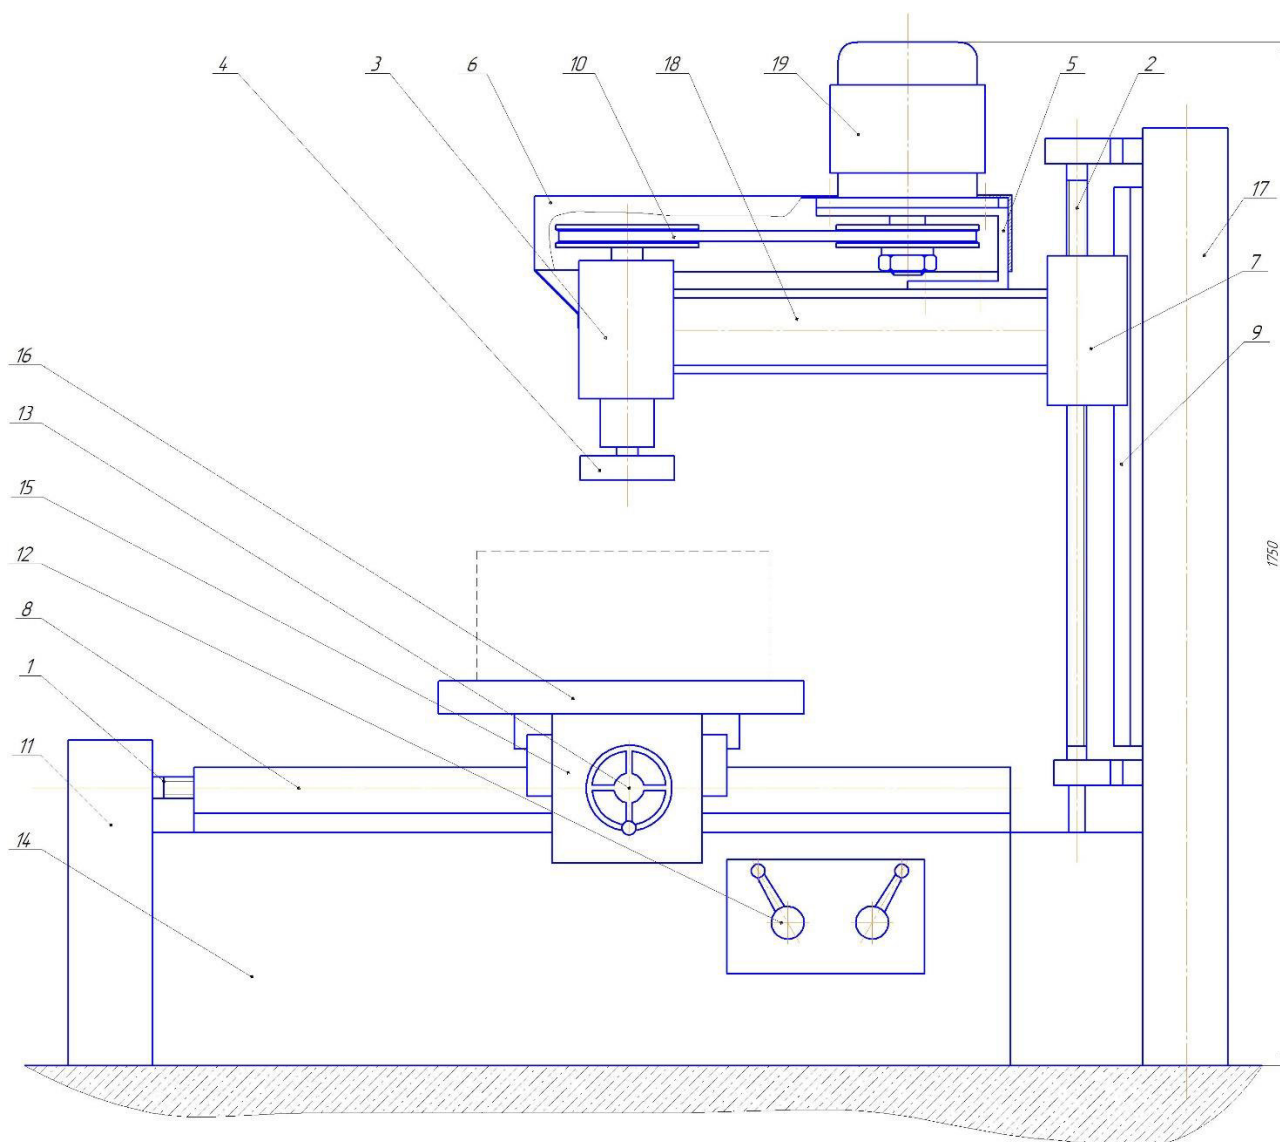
Установка для плоского шлифования головки блока цилиндров
